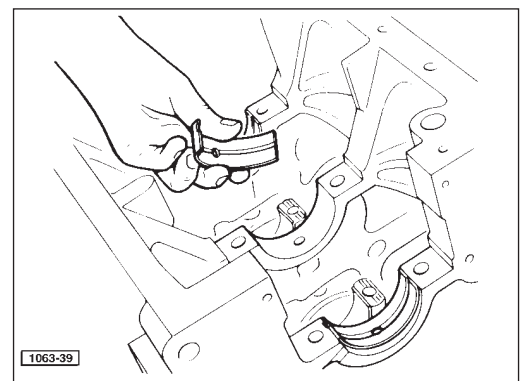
Montage des demi-coussinets de paliers dans le bloc-moteur.
